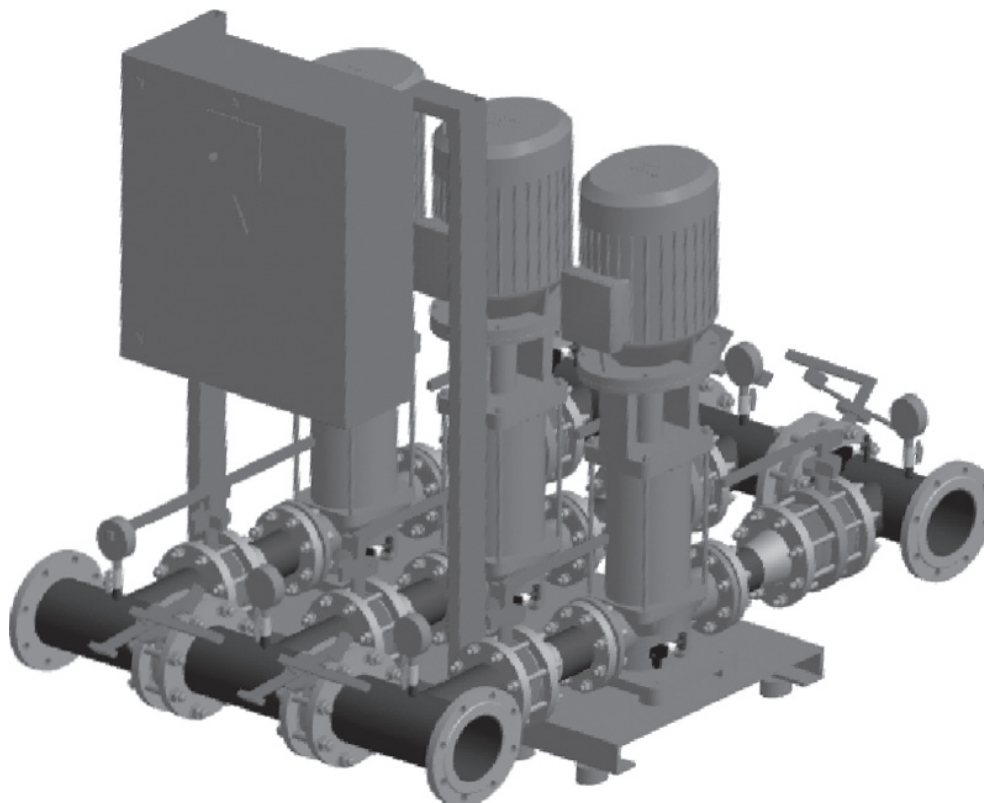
Внешний вид модульной насосной установки (МНУ) для АУП на базе насосов серии MVI... и Helix V... с прибором управления SK-FFS и без разделительных задвижек (габаритные размеры, присоединительные размеры и масса указаны в каталоге или на монтажном чертеже)
